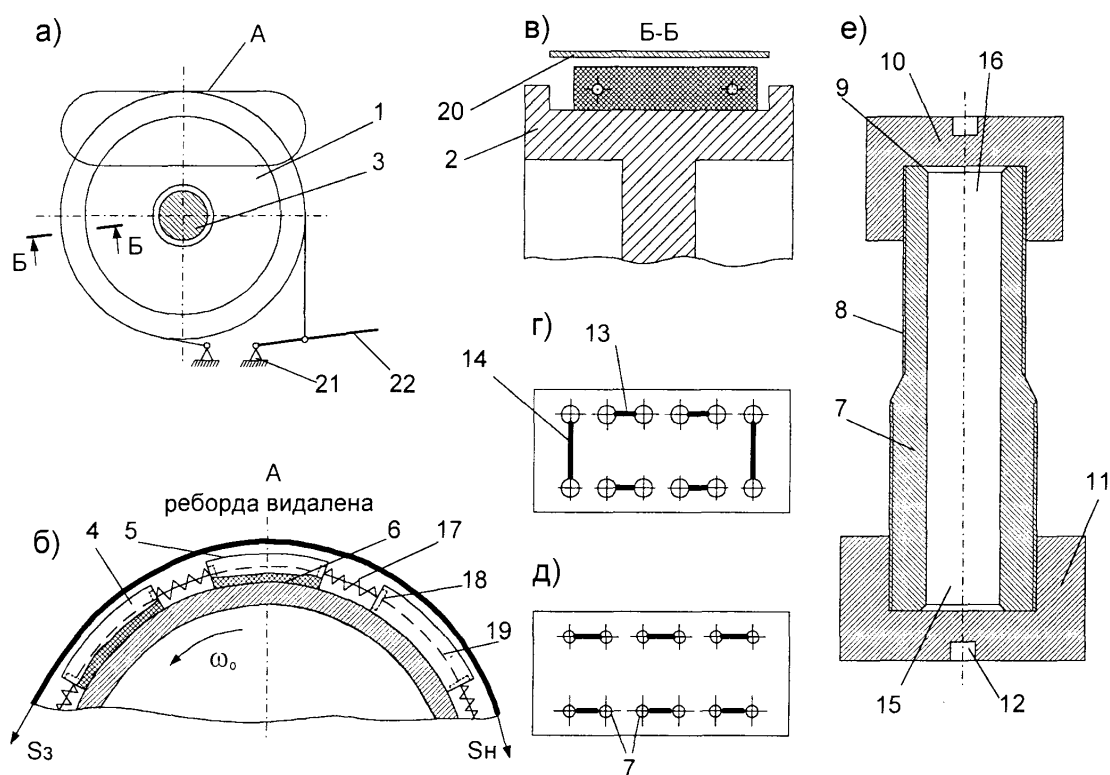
а,б,в,г,д,е Система для охолодження пар тертя стрічково-колодкових гальм з рухомими фрикційними накладками: 1, 2 – гальмівний шків з ребордами; 3 – піднімальний вал; 4, 5, 6 – фрикційні накладки з внутрішньою та зовнішньою робочими поверхнями і з набігаючими (а) і збігаючими (б) їх дільницями; 7, 8, 9, 15 і 16 – теплові труби з різьбою та торцями і з зонами випаровування та конденсації; 10, 11, 12 – гайки різних діаметрів з прорізами; 13, 14 – поздовжні та поперечні теплопровідні пластини; 17 – циліндричні пружини; 18 – направляючі отвори; 19 – циліндричні стрижні; 20 – гальмівна стрічка; 21 – корпус опори; 22 – привідний важіль
